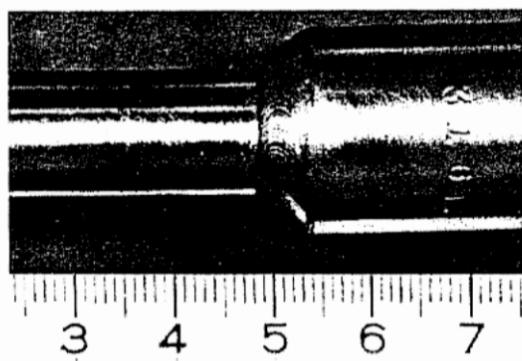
Внешний вид шва сварки углевым швом
